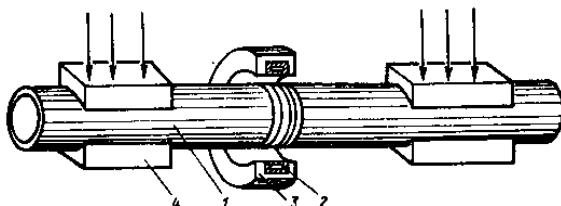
Схема высокочастотной сварки труб:
